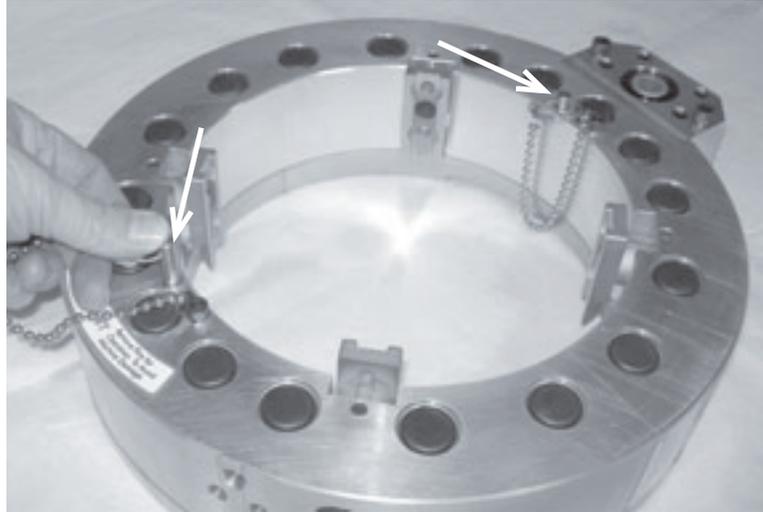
Inserire i perni di bloccaggio del telaio nella macchina.
